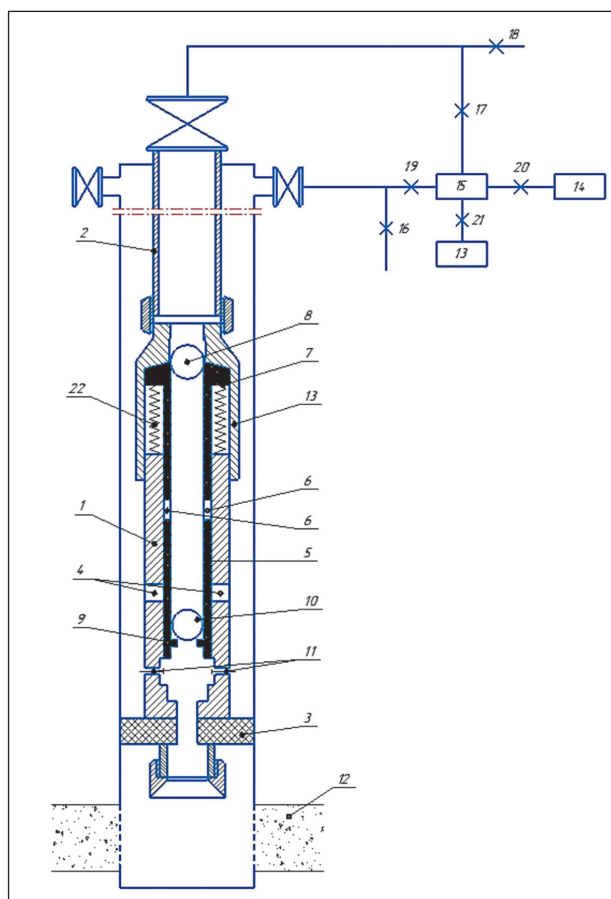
Устройство для обработки призабойной зоны скважины: 1 – корпус; 2 – НКТ; 3 – пакер; 4,6 – окно; 5 – плунжер; 7,9 – седло шара; 8, 10 – шар; 11 – циркуляционный клапан; 12 – продуктивный пласт; 13 – компрессор; 14 – продавочный агрегат; 15 – смеситель; 16 – 21 задвижки; 22 – пружина
